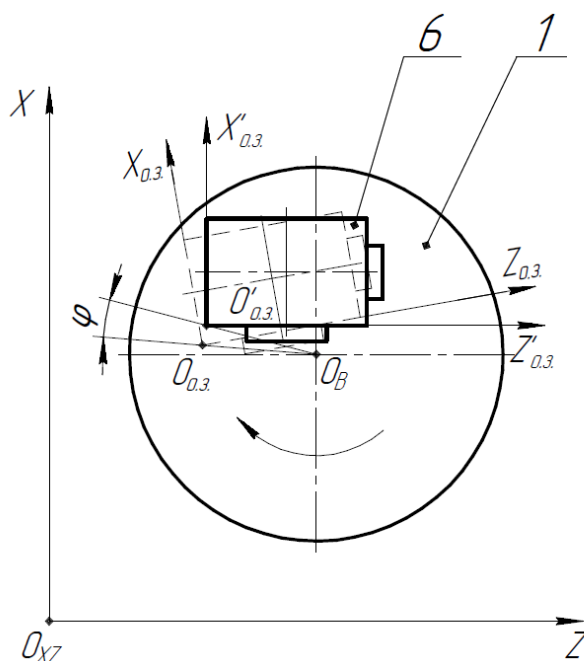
Робоче положення оброблюваної заготовки після повороту обертового стола верстата навкруги центру обертання O_B на кут φ
